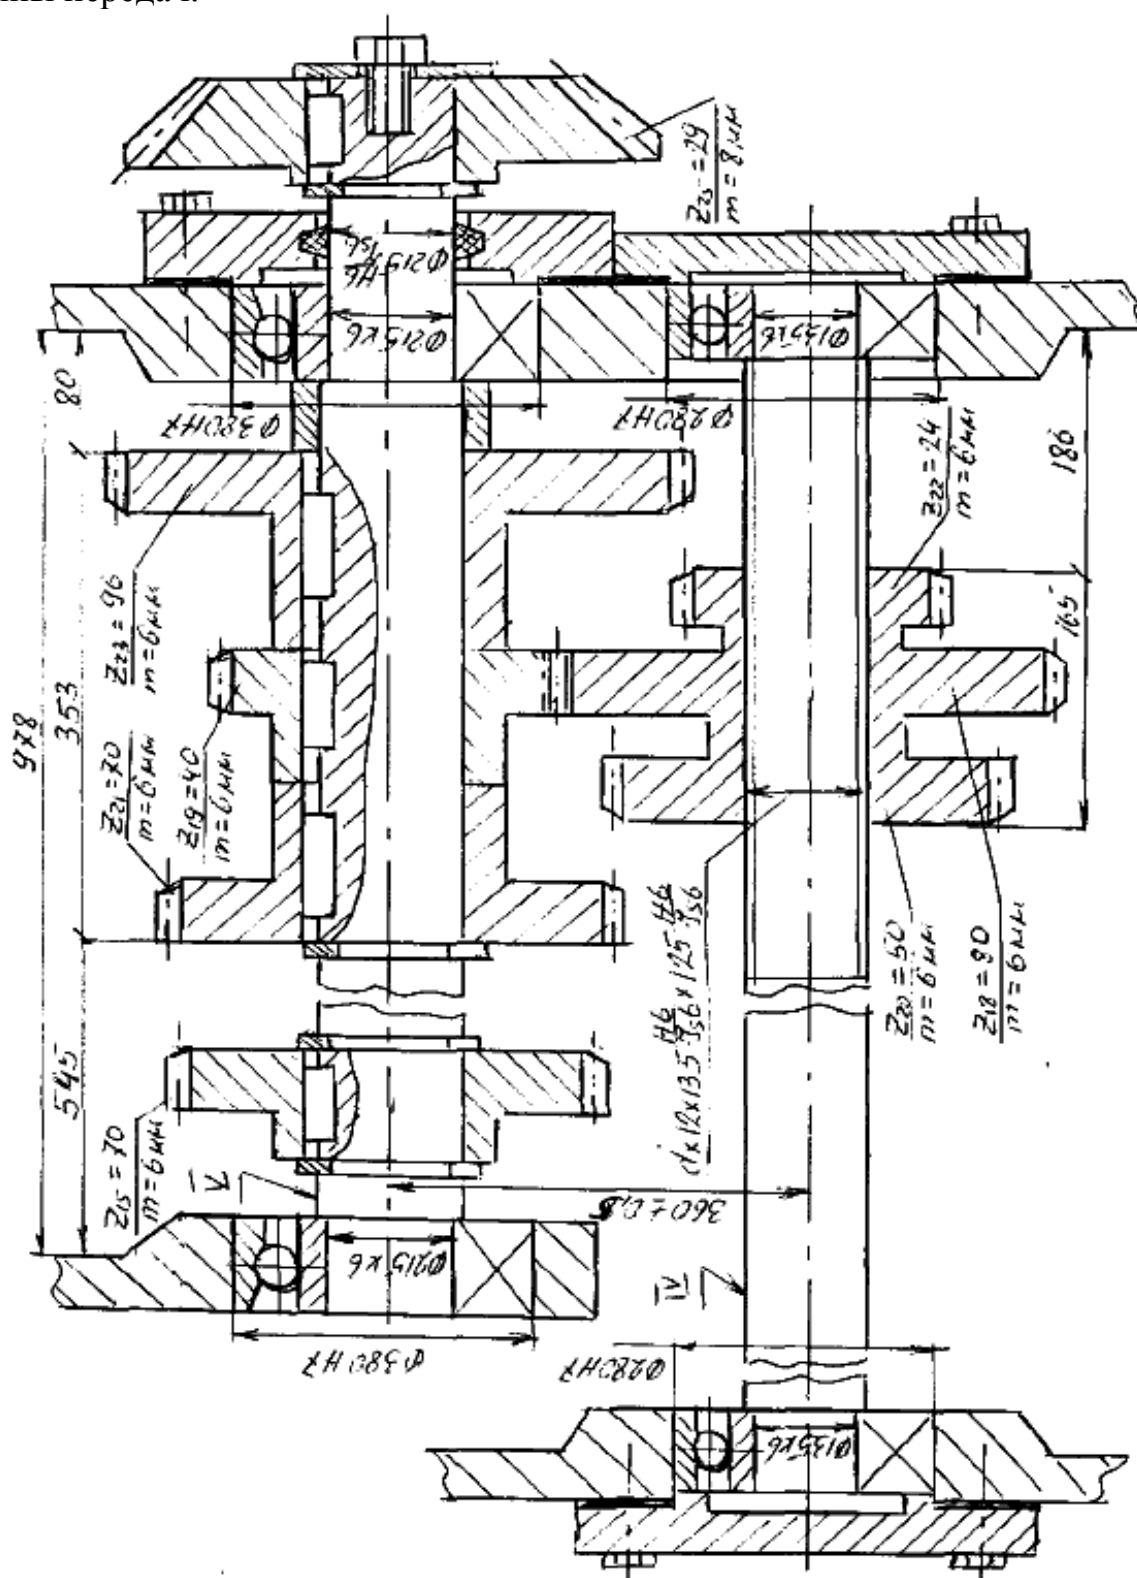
Сборочный чертеж наиболее нагруженной группы передач
